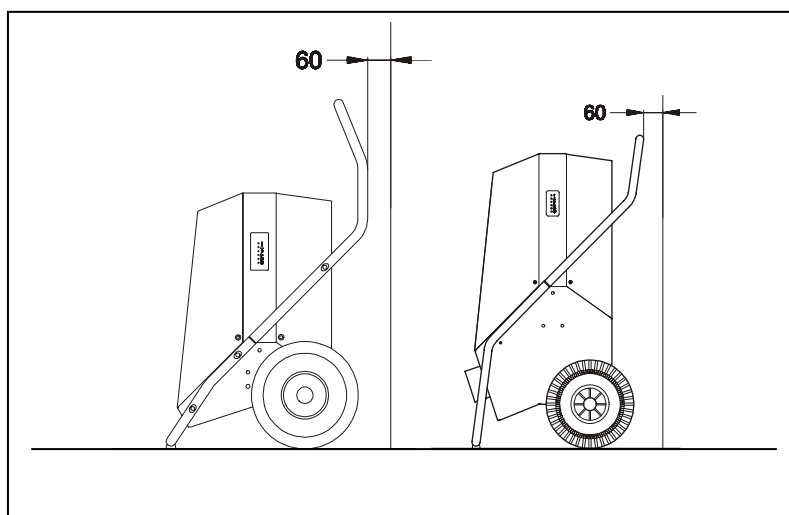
montre la mise en place de l'appareil par rapport au mur
